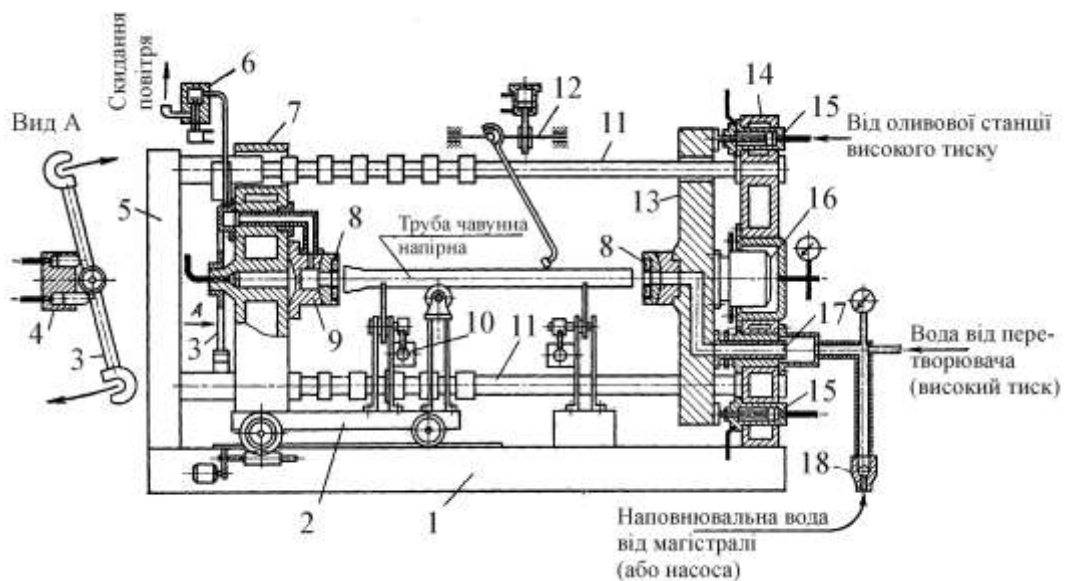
Прес для гідровипробовування труб: 1 – сталева рама; 2 – візок; 3 – замок; 4 – спарений пневмопривод; 5 – стояк; 6 – клапан скидання повітря; 7 – ліва траверса; 8 – гумові вставки; 9 – підпресовувальний механізм; 10 – випробовувана труба; 11 – колонна; 12 – синхронізатор тиску; 13 – права траверса; 14 – станція високого тиску; 15 – фіксувальний гідропривод; 16 – робочий гідропривод; 17 – перетворювач тиску; 18 – наповнювальна вода від магістралі (або насоса).
